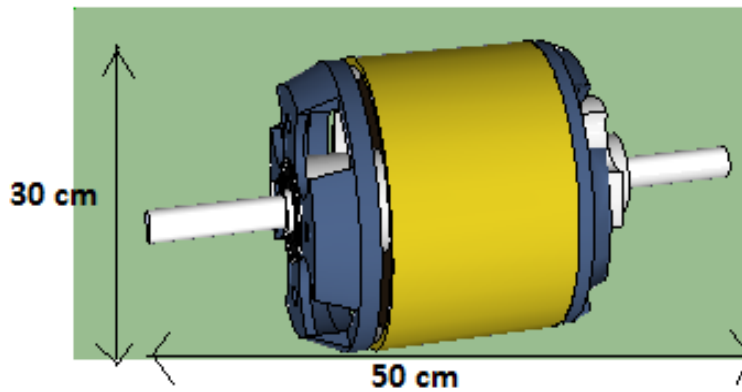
Dimensiones del motor de la máquina cortadora.
